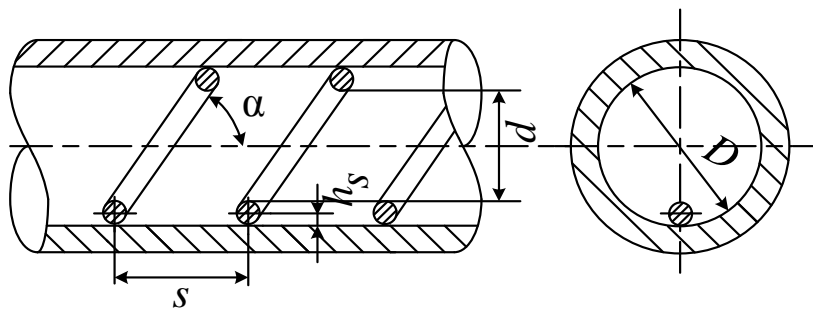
Общий вид трубы со спирально-винтовыми проволочными вставками
